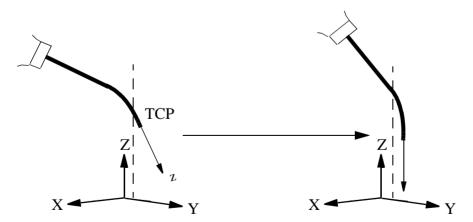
Das Werkzeug wird mit der Z-Achse ausgerichtet.
